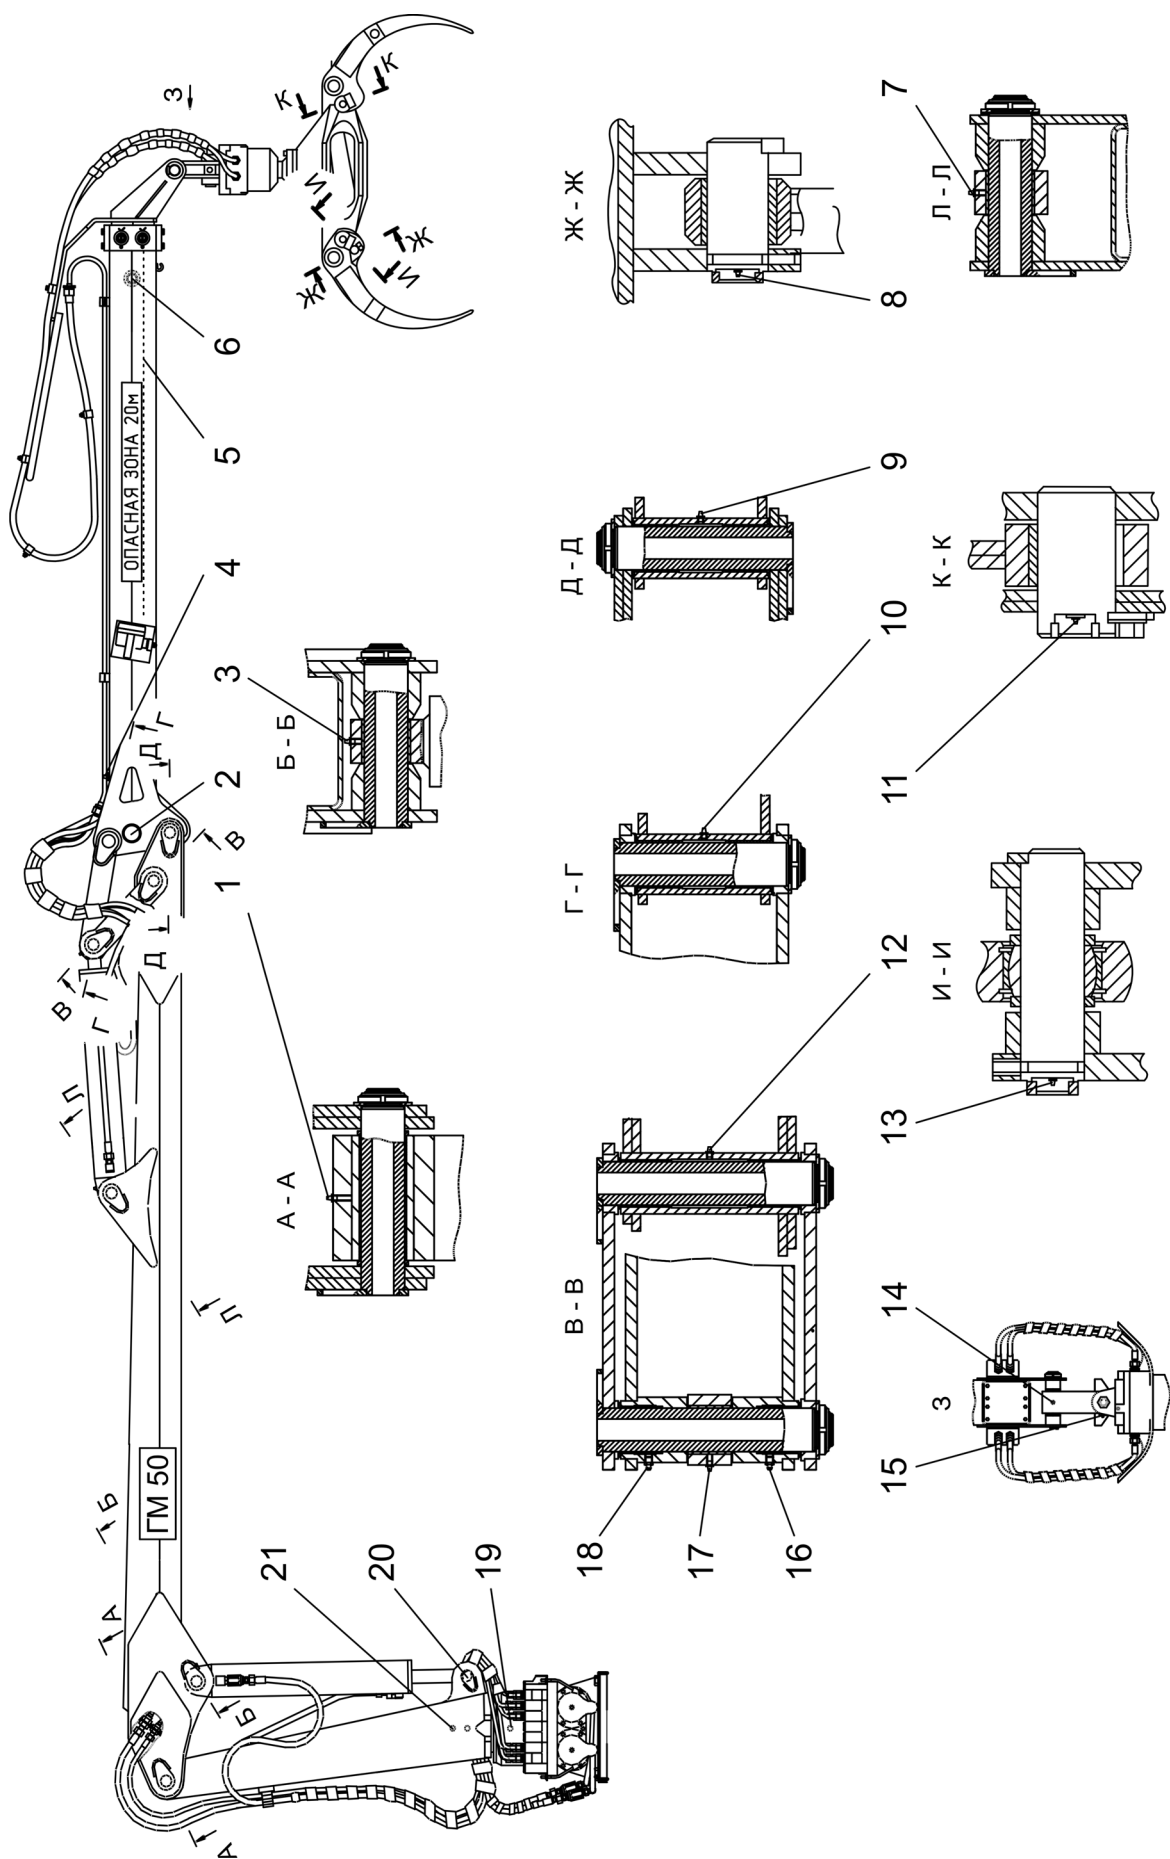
Схема смазки (заправки) манипулятора
